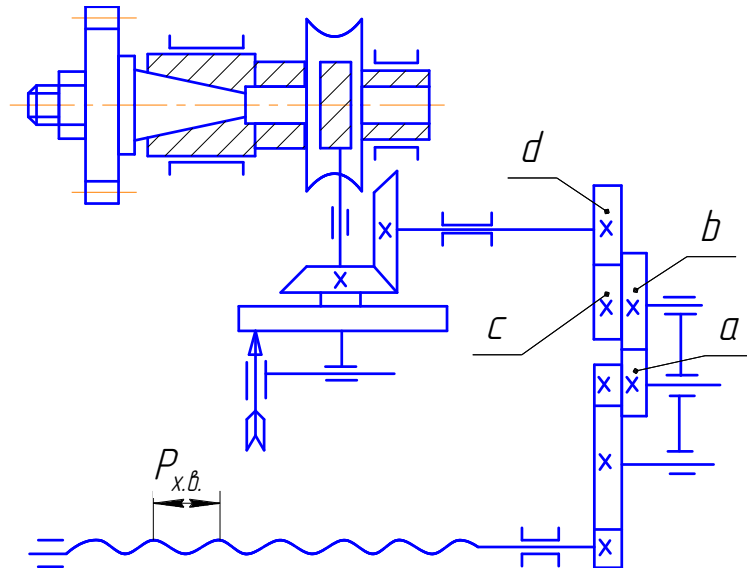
Схема настройки делительной головки на фрезерование винтового зуба
